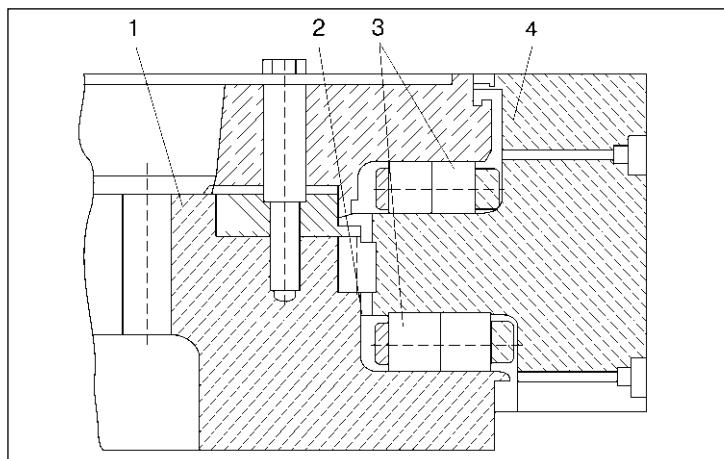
Эскиз поперечного сечения опорно-поворотного устройства в сборе: 1 — зубчатое кольцо; 2 — вертикальные ролики; 3 — горизонтальные ролики; 4 — соединительное кольцо
